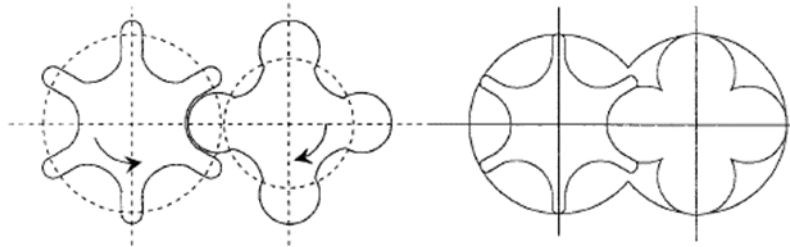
Compressores parafuso duplo com rotor macho e rotor fêmea, Stoecker [5].
